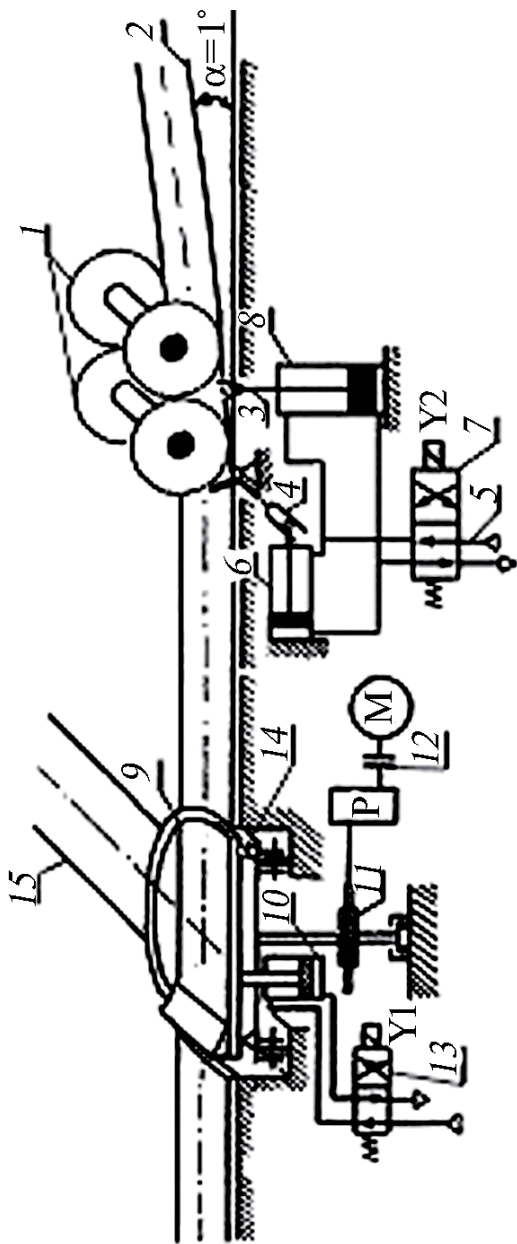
Устройство для поворота и передачи (сталкивания) колесных пар
